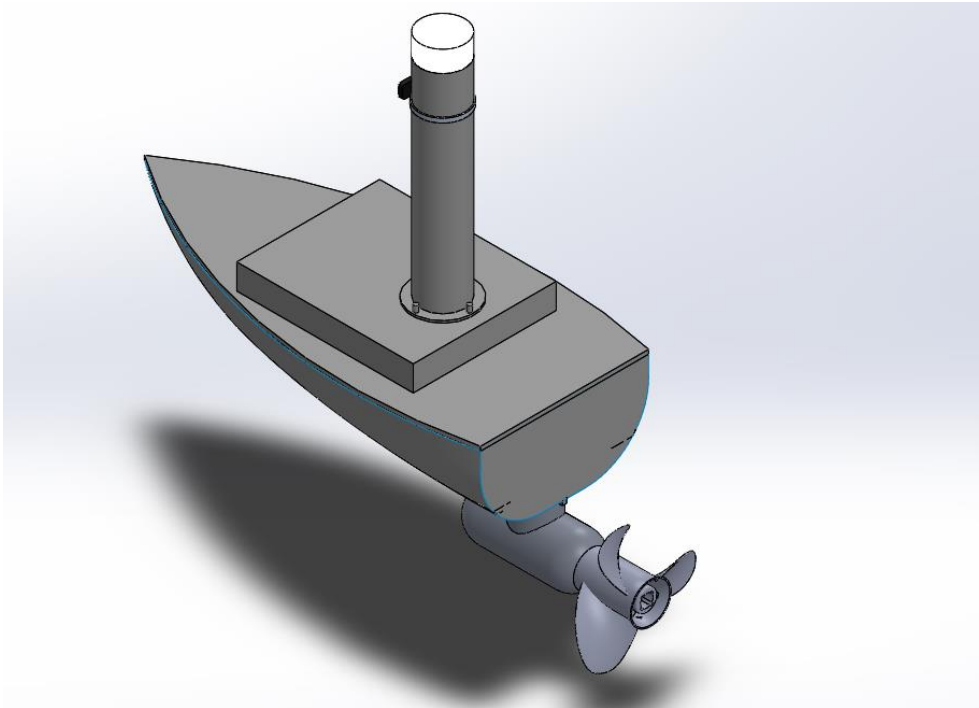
Ensamblaje final de la Alternativa 1.
